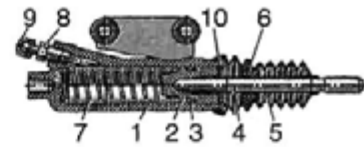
Рабочий цилиндр привода выключения сцепления:
